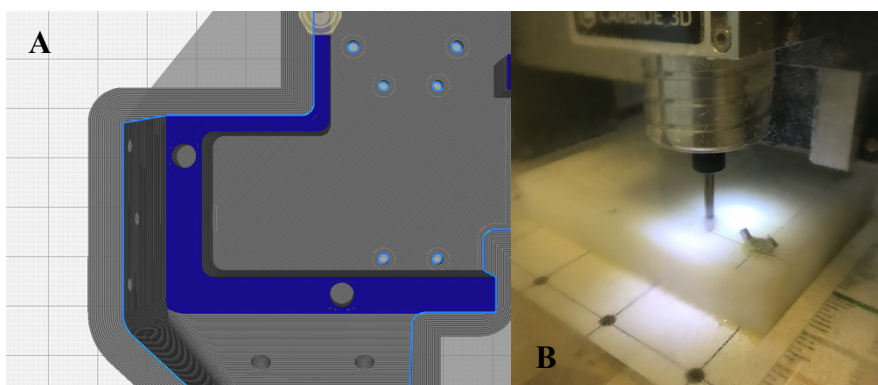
a) vista superior do chassi mostrando filetes; b) fresa em funcionamento Fonte: autora.
